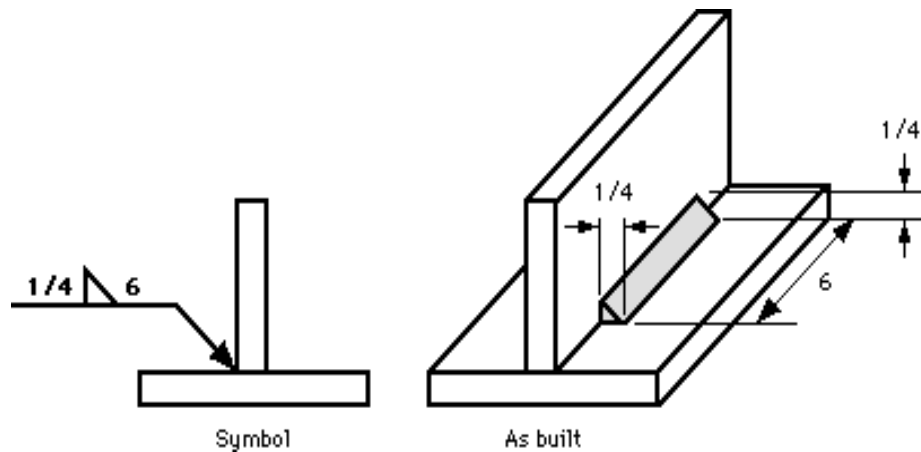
Soldadura de Filete (Longitud Del Cordón).<sup>18</sup>
